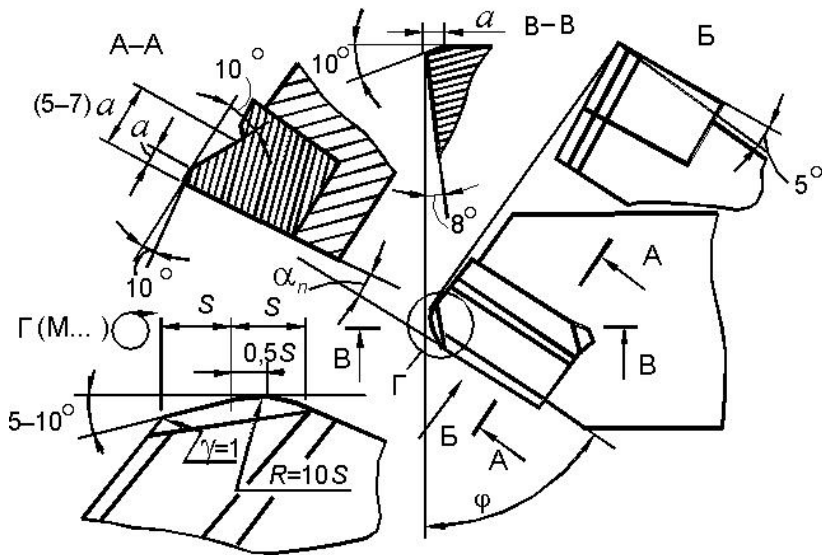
Форма режущего лезвия резца для черновой обработки сталей
